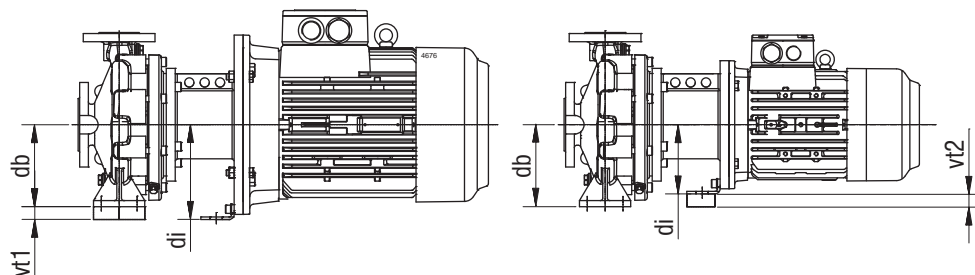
Сборка с двигателем IM 3001 (B5).
